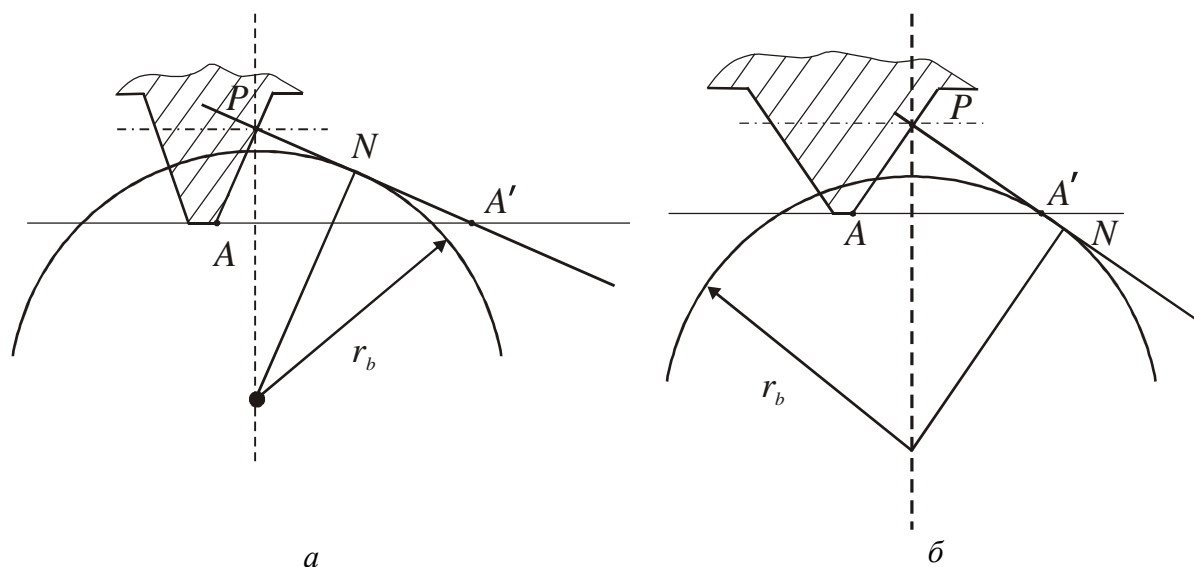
Возможные варианты расположения заготовки и рейки:
